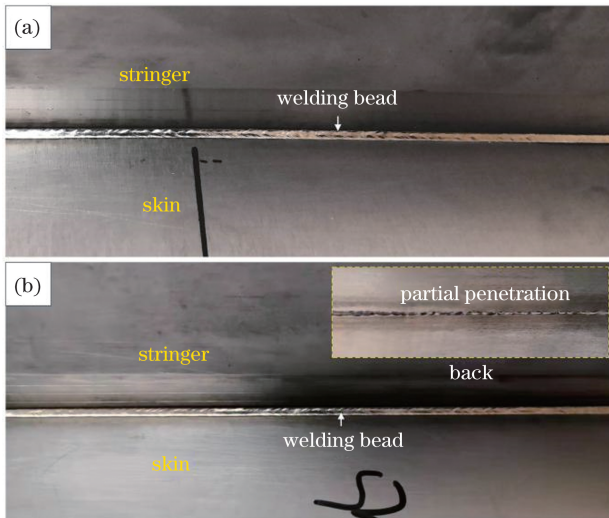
钛合金双激光束双侧同步焊接焊缝宏观成形情况。
